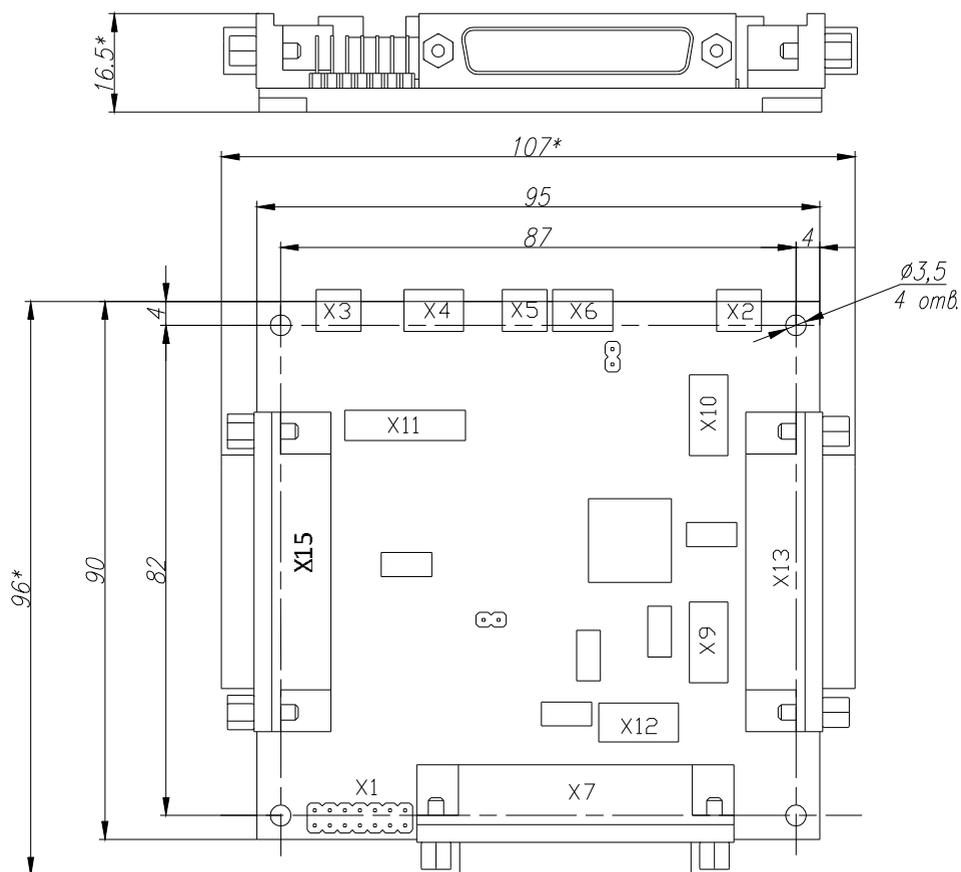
Габаритные и присоединительные размеры платы контроллера МК10.6
